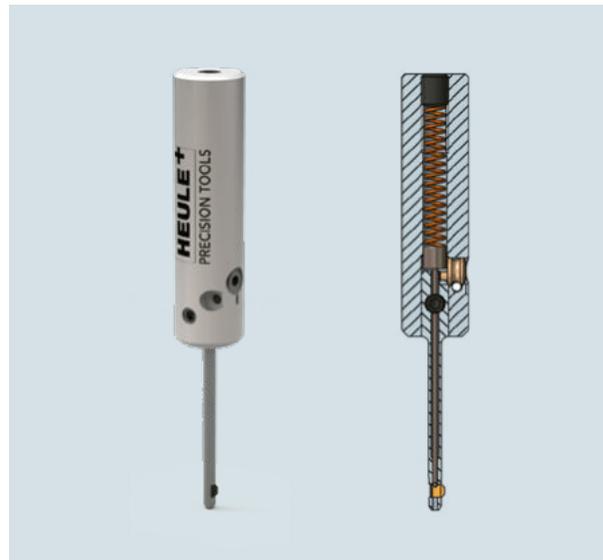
Le SNAP 2 se compose de deux pièces pour des raisons de dimension. Le corps d'outil et le porte-couteau.
